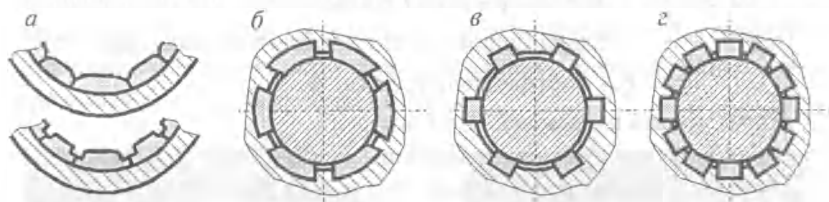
Подшипники скольжения из брусков одноосного прессования: а - набранных "в бочку"; б, в, г - запрессованных в пазы металлической обоймы (б-пазы типа "ласточкин хвост")
